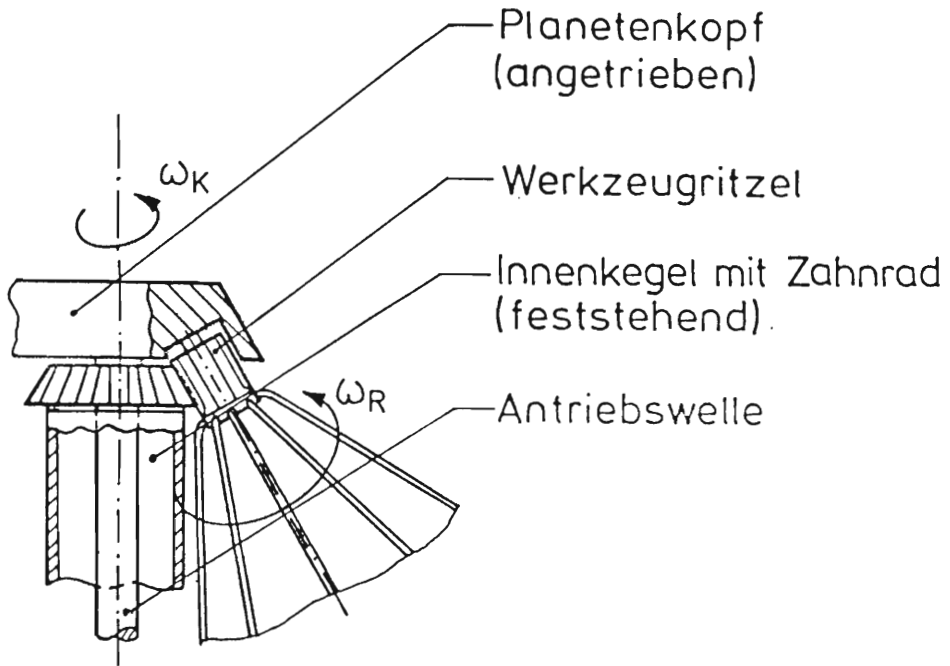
/1: Planetenkopf mit Schlagwerkzeug;
